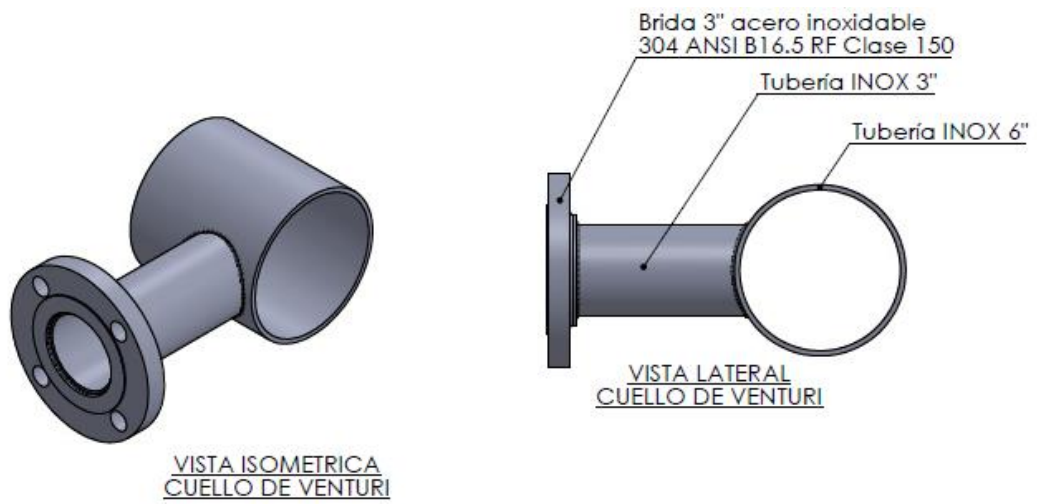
Plano detalle de cortes y construcción de garganta y entrada de succión
